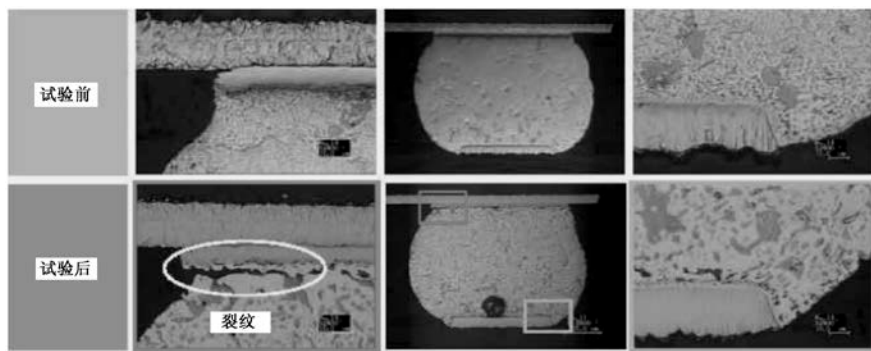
BGA (Sn-37Pb) 焊球 + SAC305 焊膏的温度循环试验
